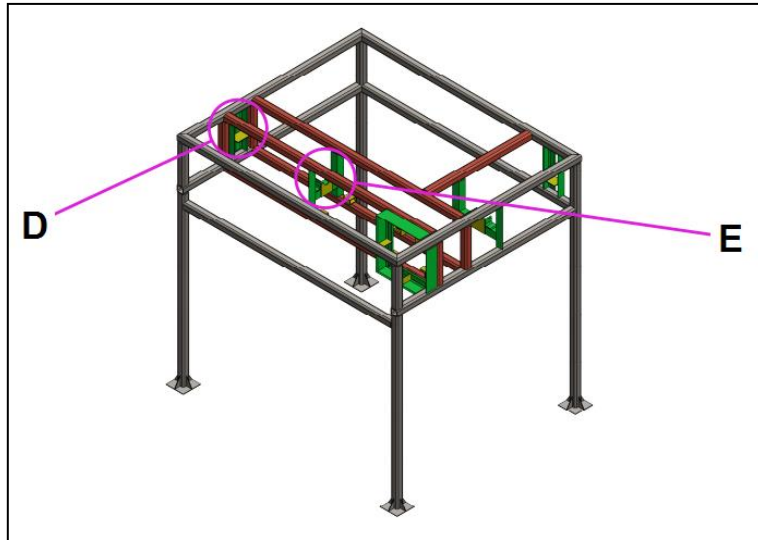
Vista de las secciones D y E de la estructura de la peladora y picadora de piñas
